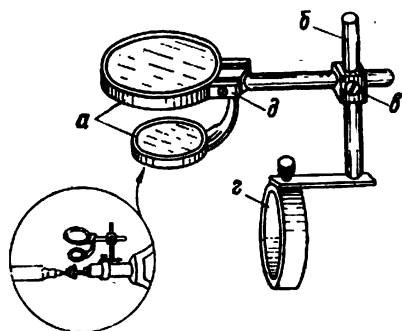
Приспособление к токарному станку: а — увеличительное стекло; б — штанга; в — движок; г — кольцо с винтом, закрепляемое на спице токарного станка; д — винт
